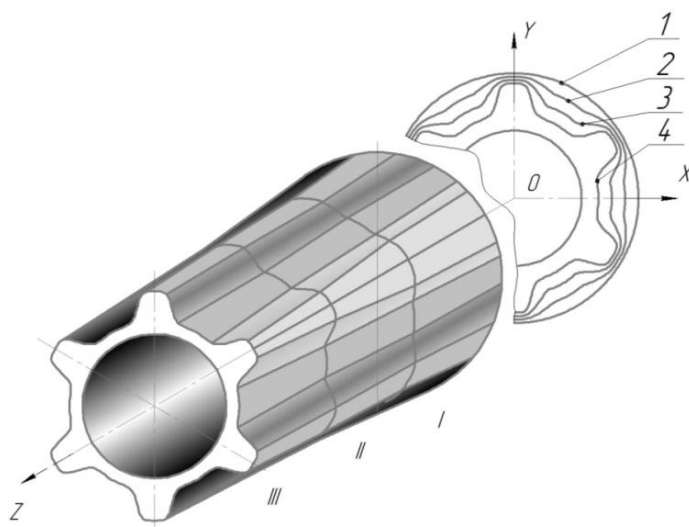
Последовательность формоизменения металла в очаге деформации при волочении в три перехода криволинейного профиля: 1 – наружный диаметр заготовки, 2 и 3 – эквипотенциали промежуточных первого и второго переходов, 4 – контур готовой трубы. I, II и III – продольные профили волок первого, второго и третьего переходов
